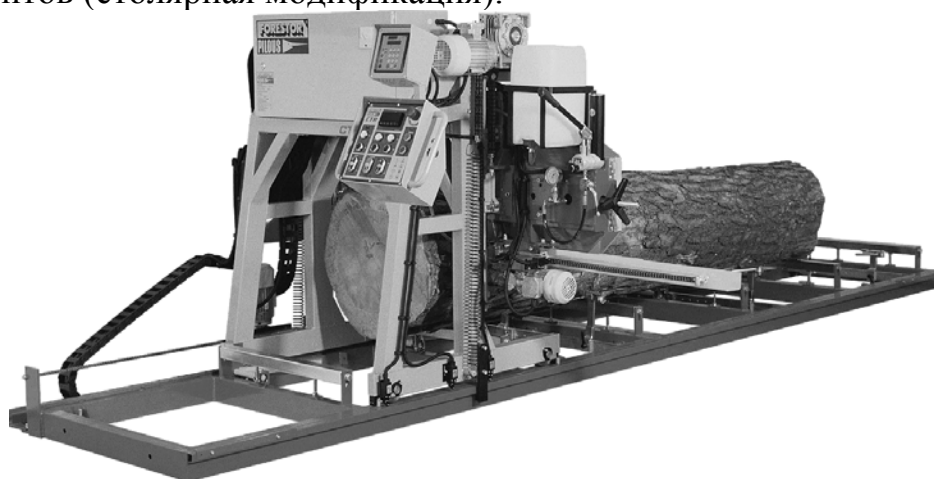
Общий вид бревнопильного ленточнопильного станка
